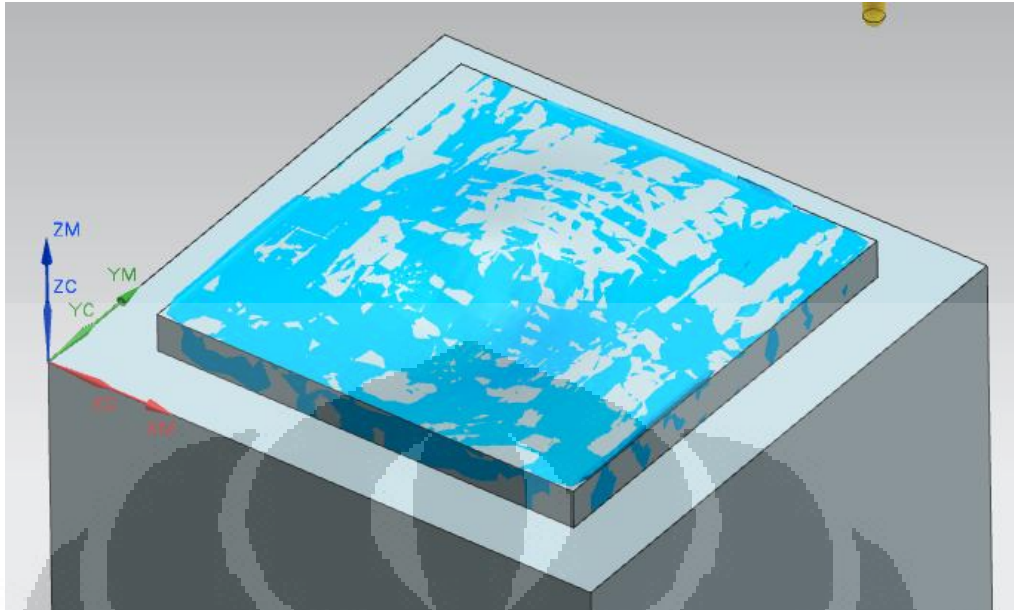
Geometri hasil pemesinan *semi finishing* dengan pahat 0.2 mm *flat end mill* secara aktual
